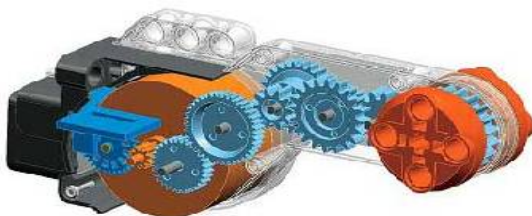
VISTA INTERNA DEL MOTORE LEGO
